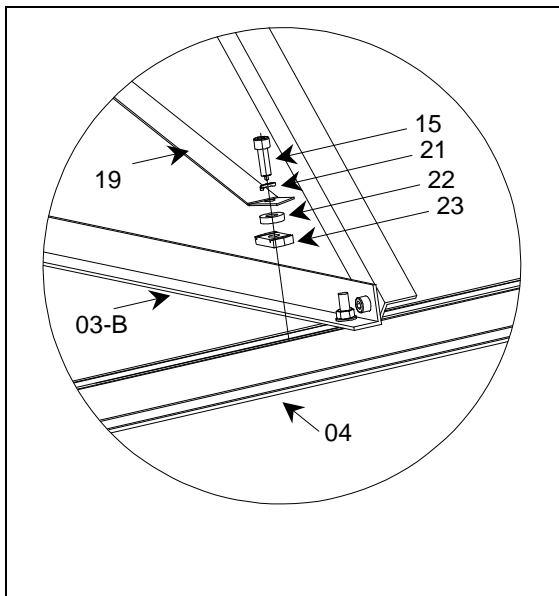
Befestigung Sicherungskreuz-Basisprofil
